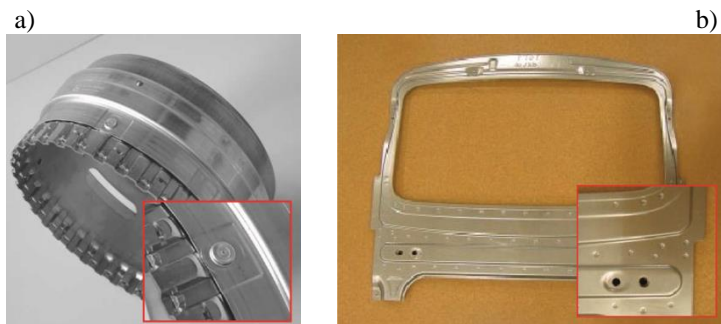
Implementacja przetłaczania w konstrukcji fotela:
